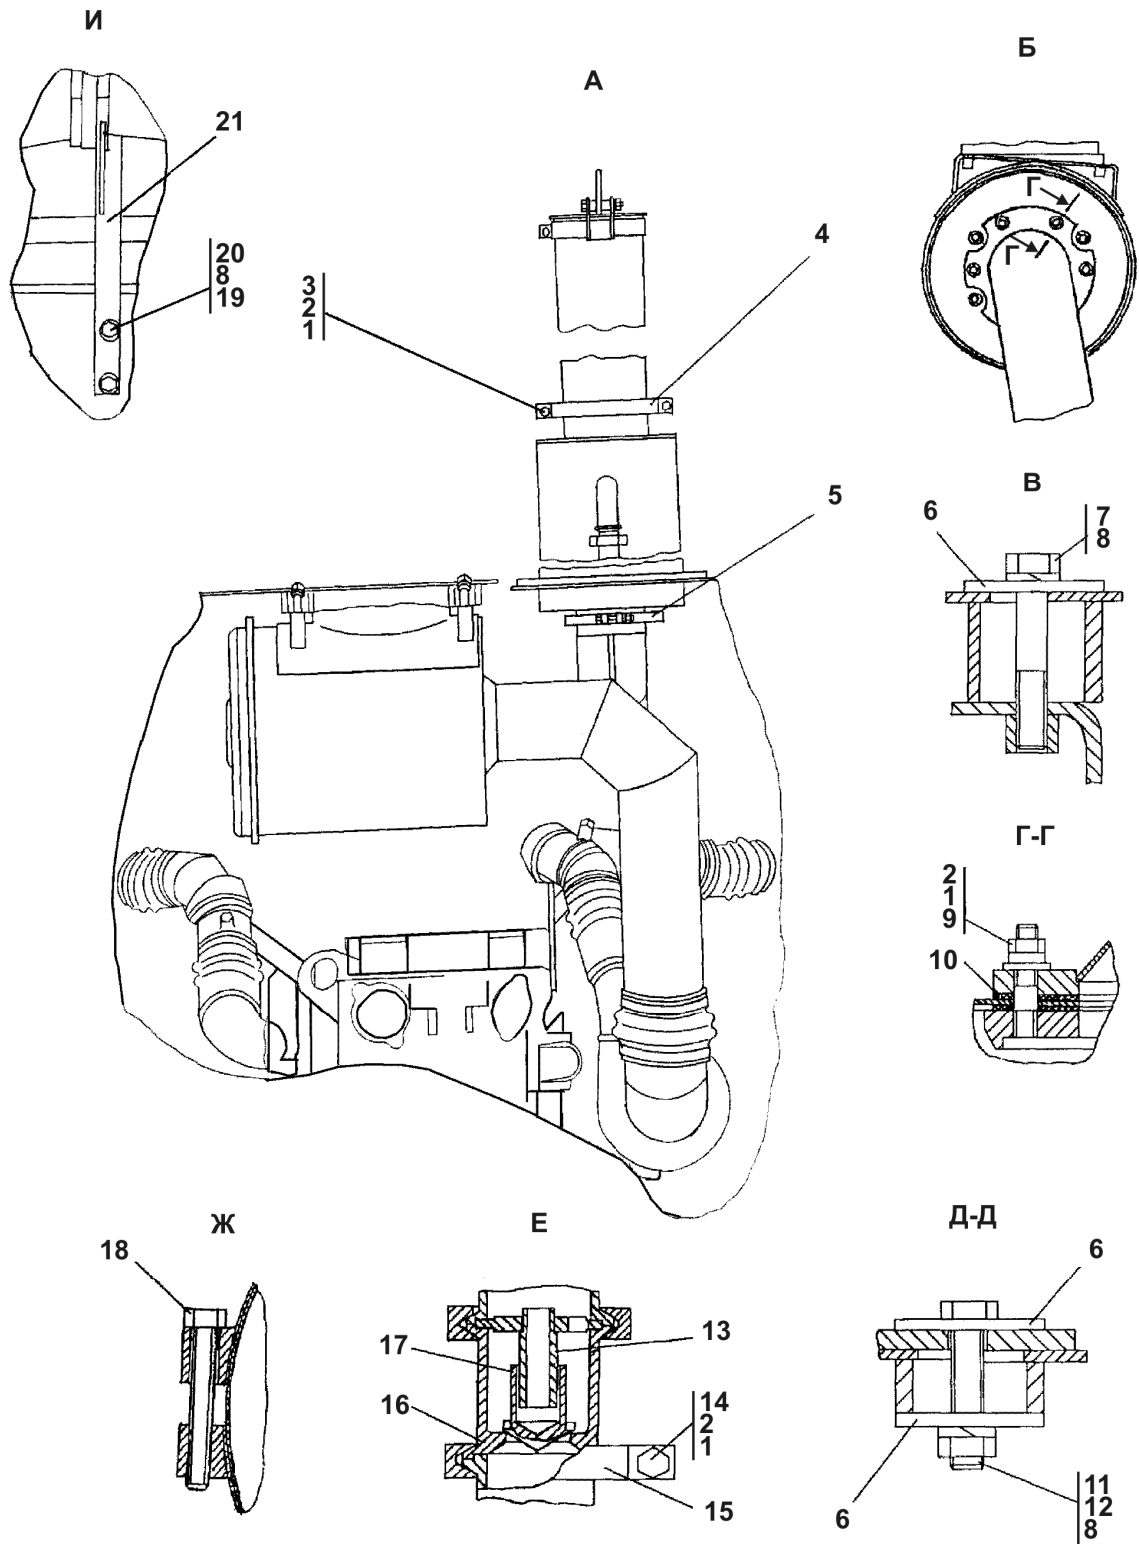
Установка систем воздухоочистки и выпуска
